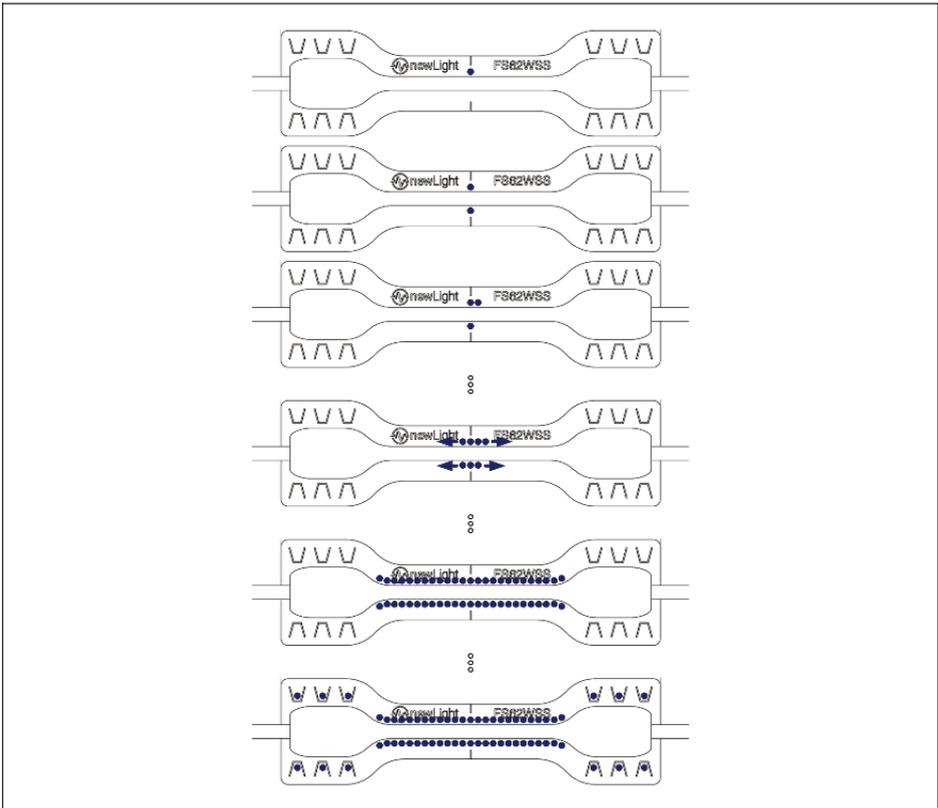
Schweißverfahren für FS62WSS
